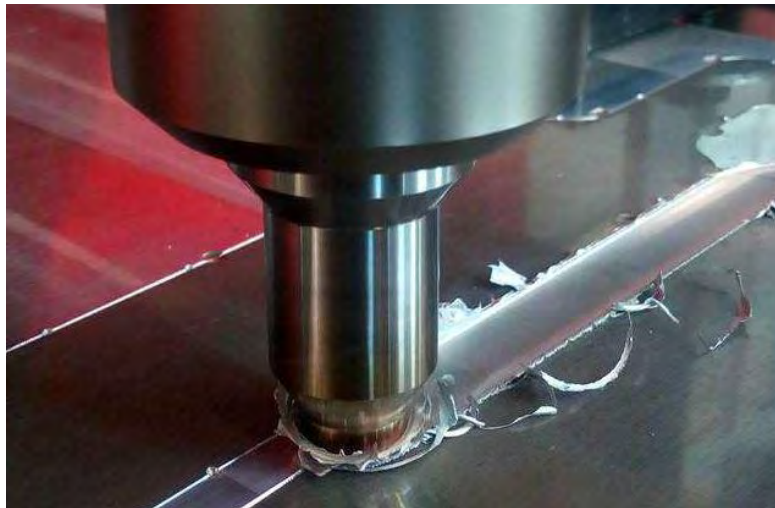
Процес зварювання титанового сплаву та контроль якості зварювання
